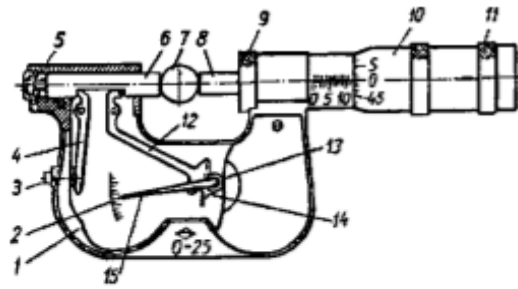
Важільний мікрометр: 1 – скоба; 2 – шкала; 3 – кнопка; 4 – важіль; 5 – пружина; 6 – п'ятка; 7 – виріб; 8 – мікрометричний гвинт; 9 – стопорний пристрій; 10 – барабан; 11 – ковпачкова гайка; 12 – важіль; 13 – зубчасте колесо; 14 – спіральна пружина; 15 – стрілка
